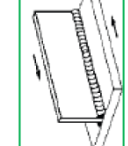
Schweißnahtdetail T_YB_EF
